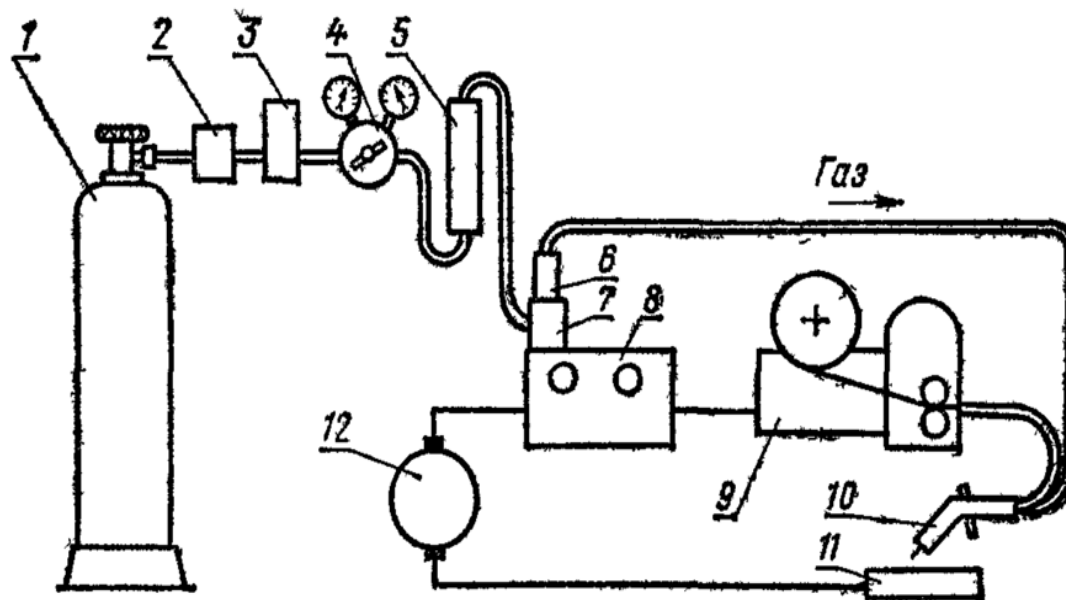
Схема установки для напівавтоматичного зварювання або наплавлення в середовищі вуглекислого газу:
